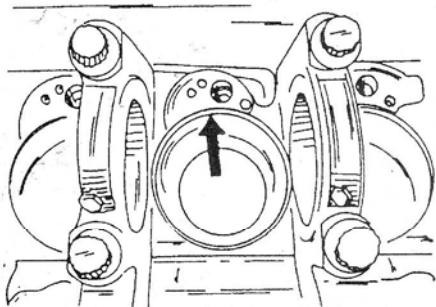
Стрелка указывает местоположение форсунок впрыска масла охлаждения поршней на названных двигателях.
